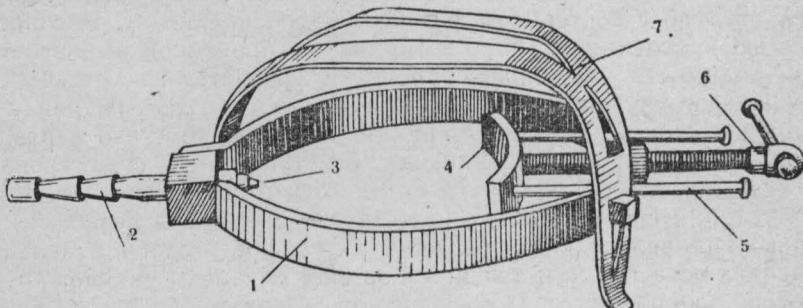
Приспособление для гидравлических испытаний корпусов огнетушителей через спрыск, конструкции И. Москаlevа:
